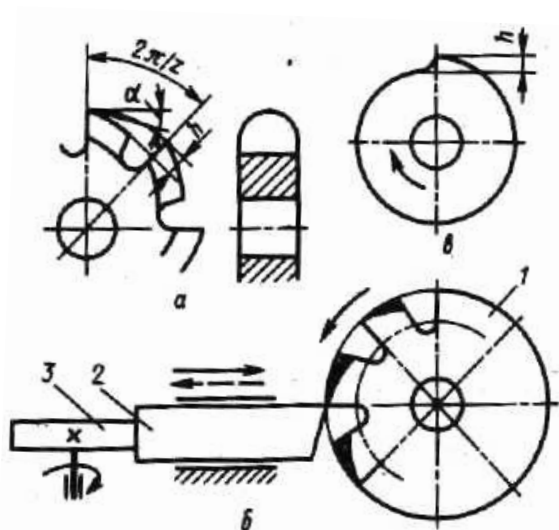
Схема затылования зубьев дисковой фрезы
